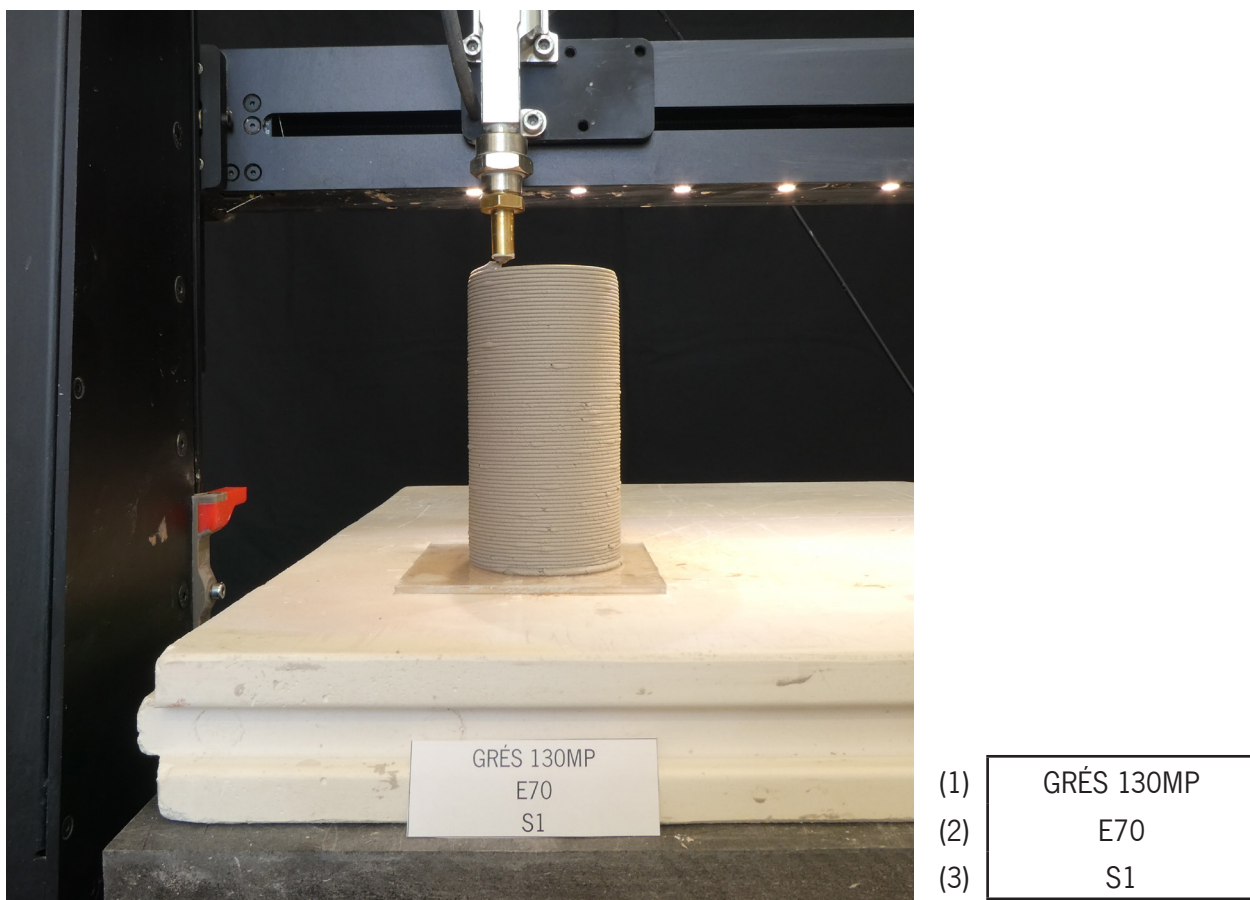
Equipamento Lutum@v4.3 MXL Clay Printer.
